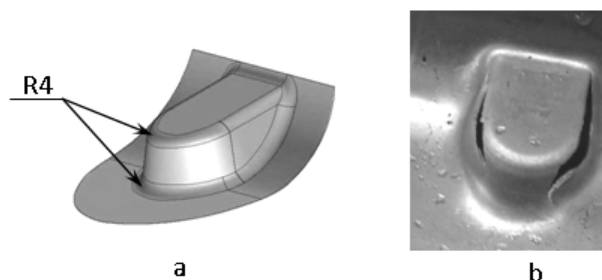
3D модель бобышки (а) с прилегающей зоной, вовлеченной в процесс ее формообразования и трещины на бобышке (б), изготовленной в матрице без предварительной формовки
